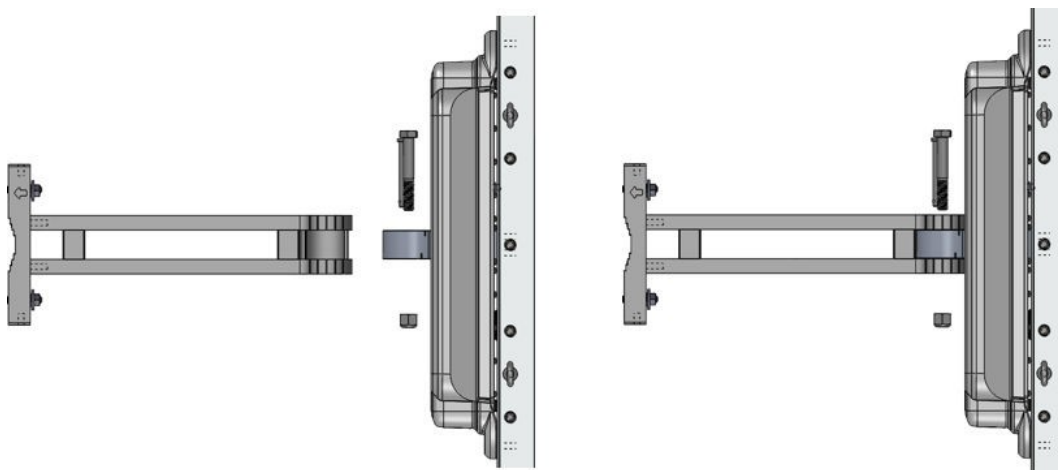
Montage der Solarpanel-Baugruppe am Montagearm
